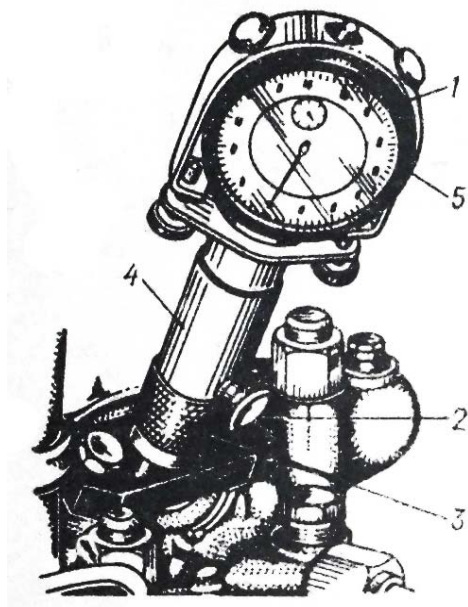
Вимірювання сумарного зазору в шатунних підшипниках приладом КИ – 13933М: 1 – скоба; 2 – гвинт; 3 – механізм подачі вимірювальної струни; 4 – корпус; 5 – індикатор.
